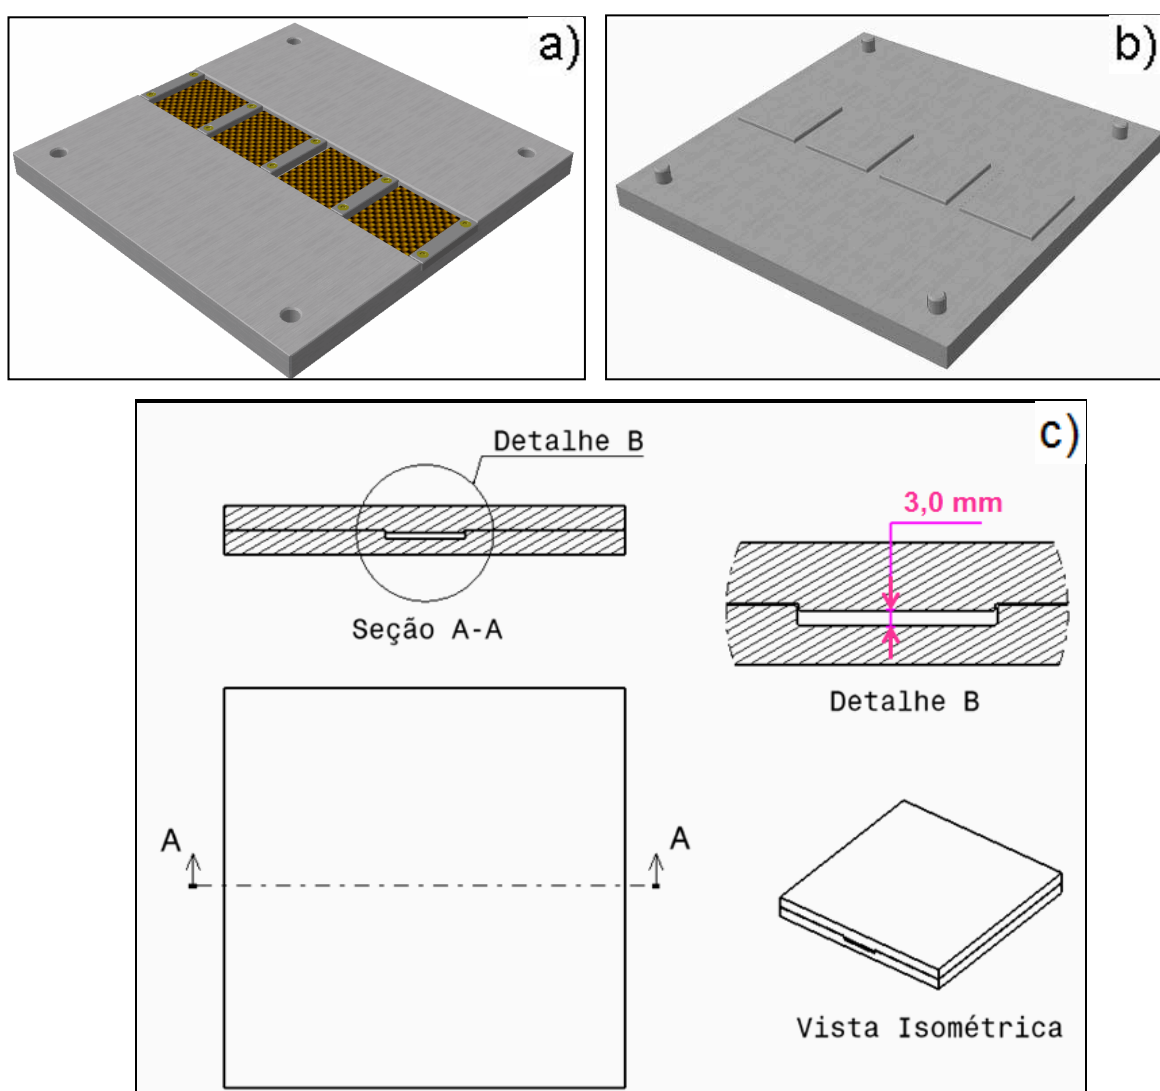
Conjunto de moldes utilizados para a consolidação dos compósitos a partir do processo de moldagem por compressão a quente: a) parte inferior - fêmea (com compósito consolidado); b) parte superior – macho e c) detalhe do conjunto de moldes montados projetado para obter corpos-de-prova com espessura de 3mm.
